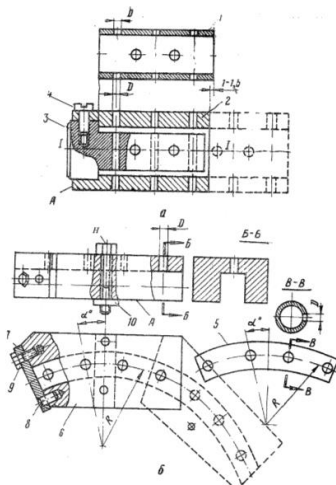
Схемы сверления отверстий с применением шагающего кондуктора в коротких и длинных трубках: а – прямых; б – изогнутых по радиусу R
